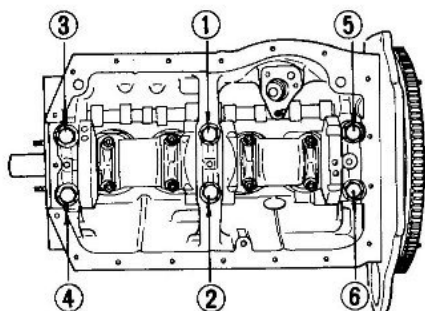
Chapeaux et coussinets de paliers de vilebrequin
